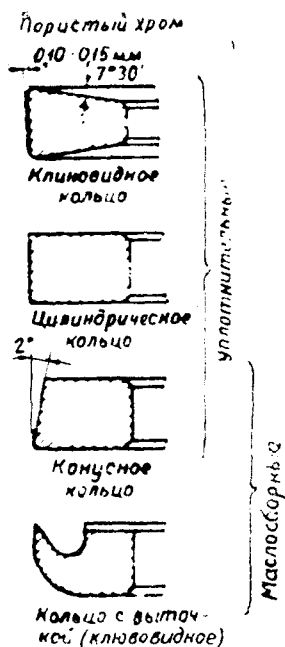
Типы поршневых колец и расположение их на поршне: а — клиновидное; б — конусное; в — с выточкой (ключовидное)
